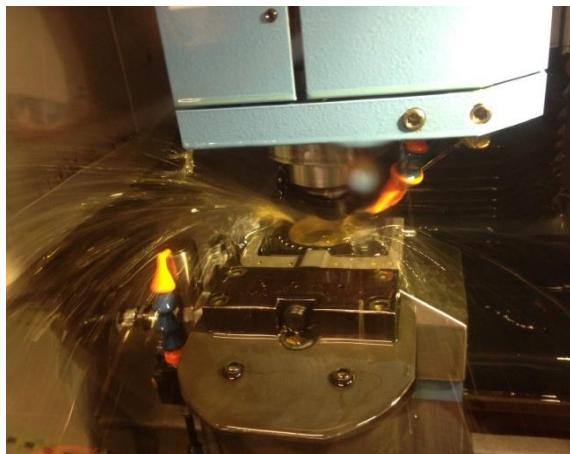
Nach jedem Arbeitsschritt – Spanen, Fräsen, Bohren – ist ein Schleifgang erforderlich, bei dem die Platinen auf die entsprechende Tiefe plan geschliffen werden.
